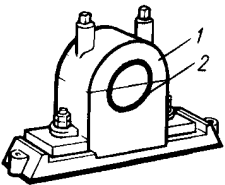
Подшипник скольжения: 1 — корпус подшипника; 2 — вкладыш; 3 — вал; 4 — отверстие для смазки
